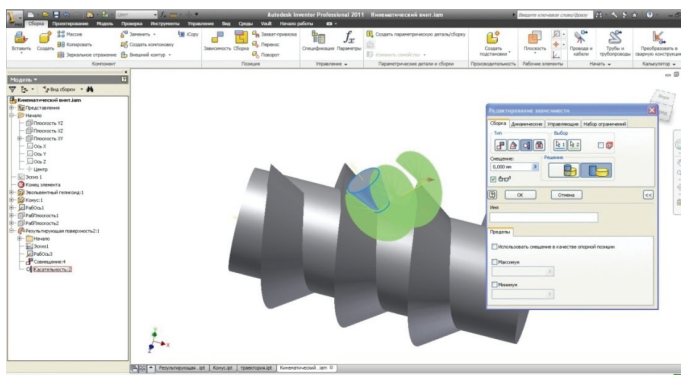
Готова тривимірна модель спряжених поверхонь «евольвентний гелікоїд – конус обертання»
